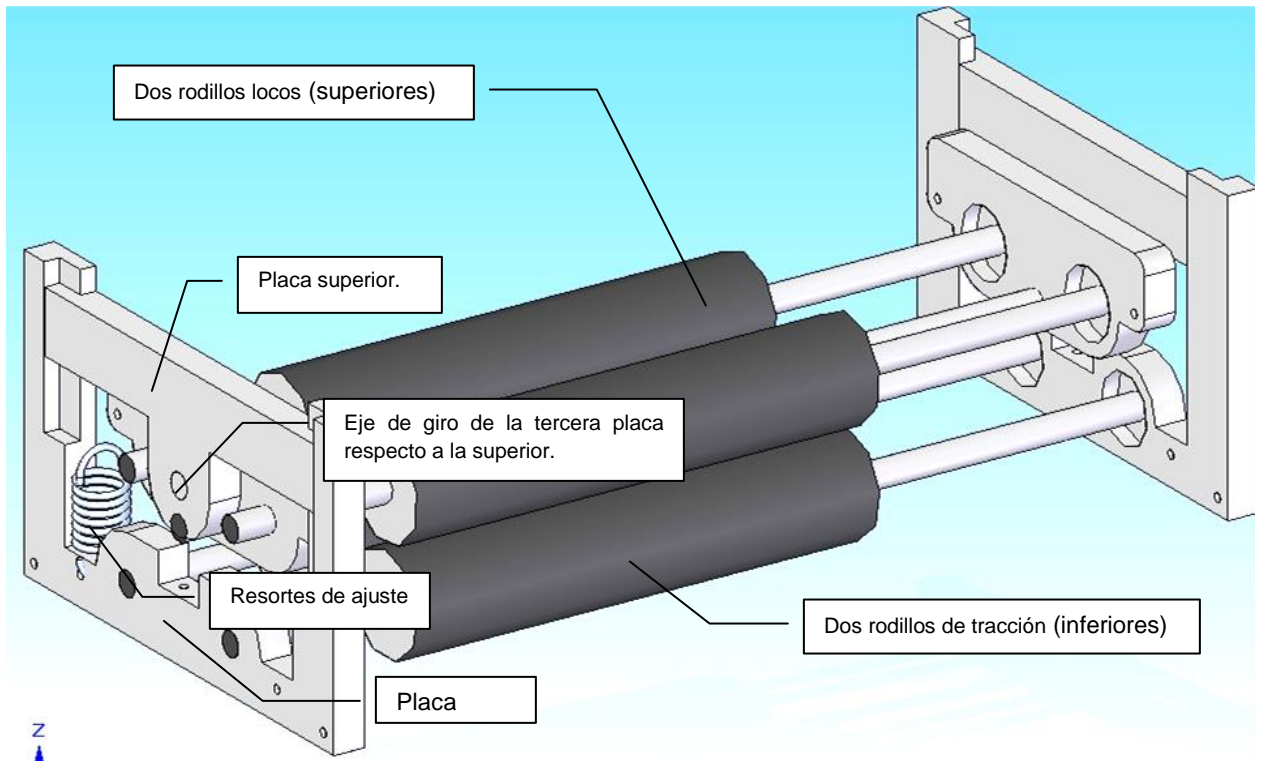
Vista isométrica del módulo de desespinado y breve descripción de los componentes de ensamble.
